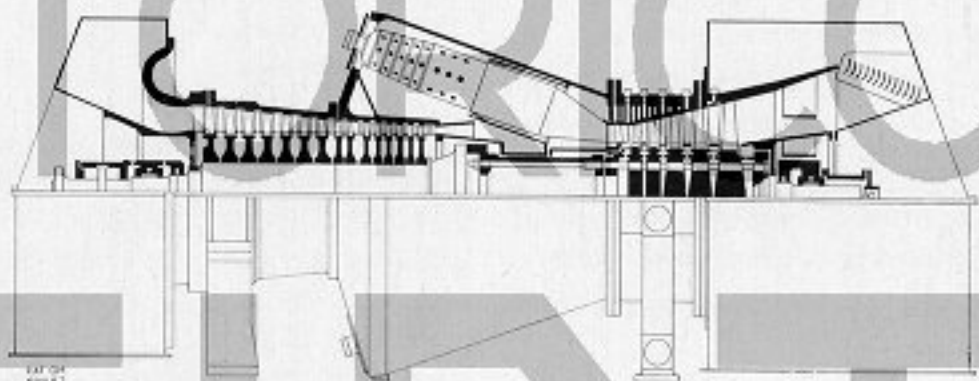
Turbina a gas TG 16. Sezione longitudinale
